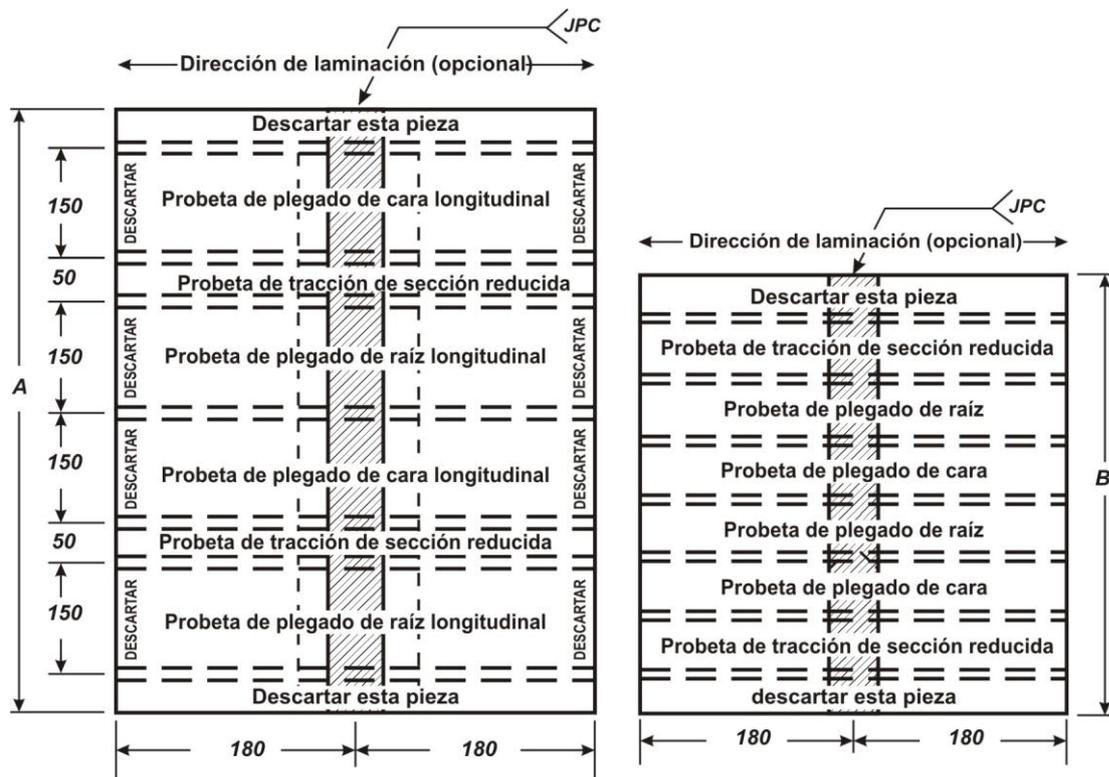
Ubicación de las probetas de ensayo para el tubo de sección rectangular.
